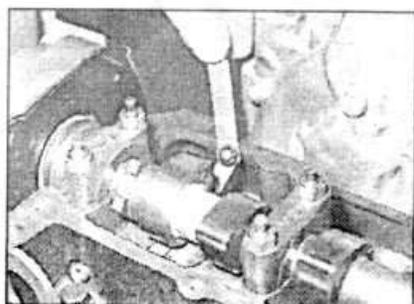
Е.1. Проверка и регулировка зазора клапанов.
